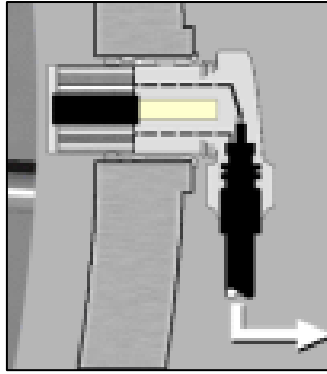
Sensor de posición del cigüeñal. Fuente: (Chrysler AG, 2005)
